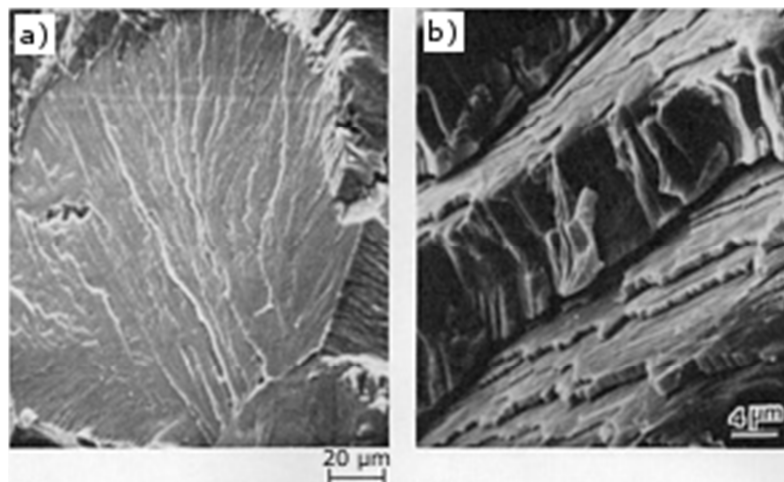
a) Patrón de plumas en un cristal de acero al cromo fracturado por clivaje. b) Escalones de clivaje en una aleación Al-Cu fracturada que falló por fractura transgranular bajo corrosión-tensión. Fuente [51].
